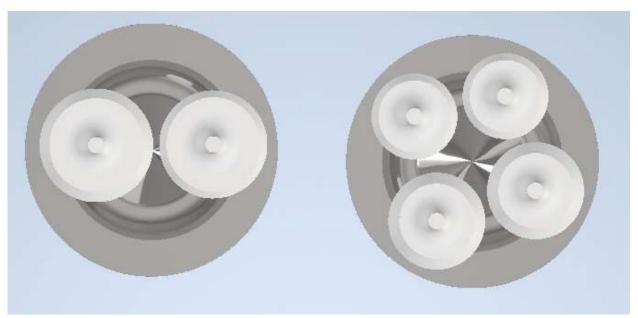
Эскизная компоновка двух и четырех клапанов в ГБЦ в SolidWorks
